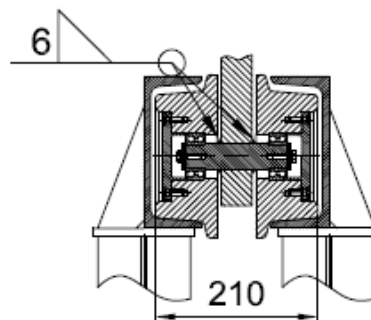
BG7, 8 und 9; Detail Radaufhängung
